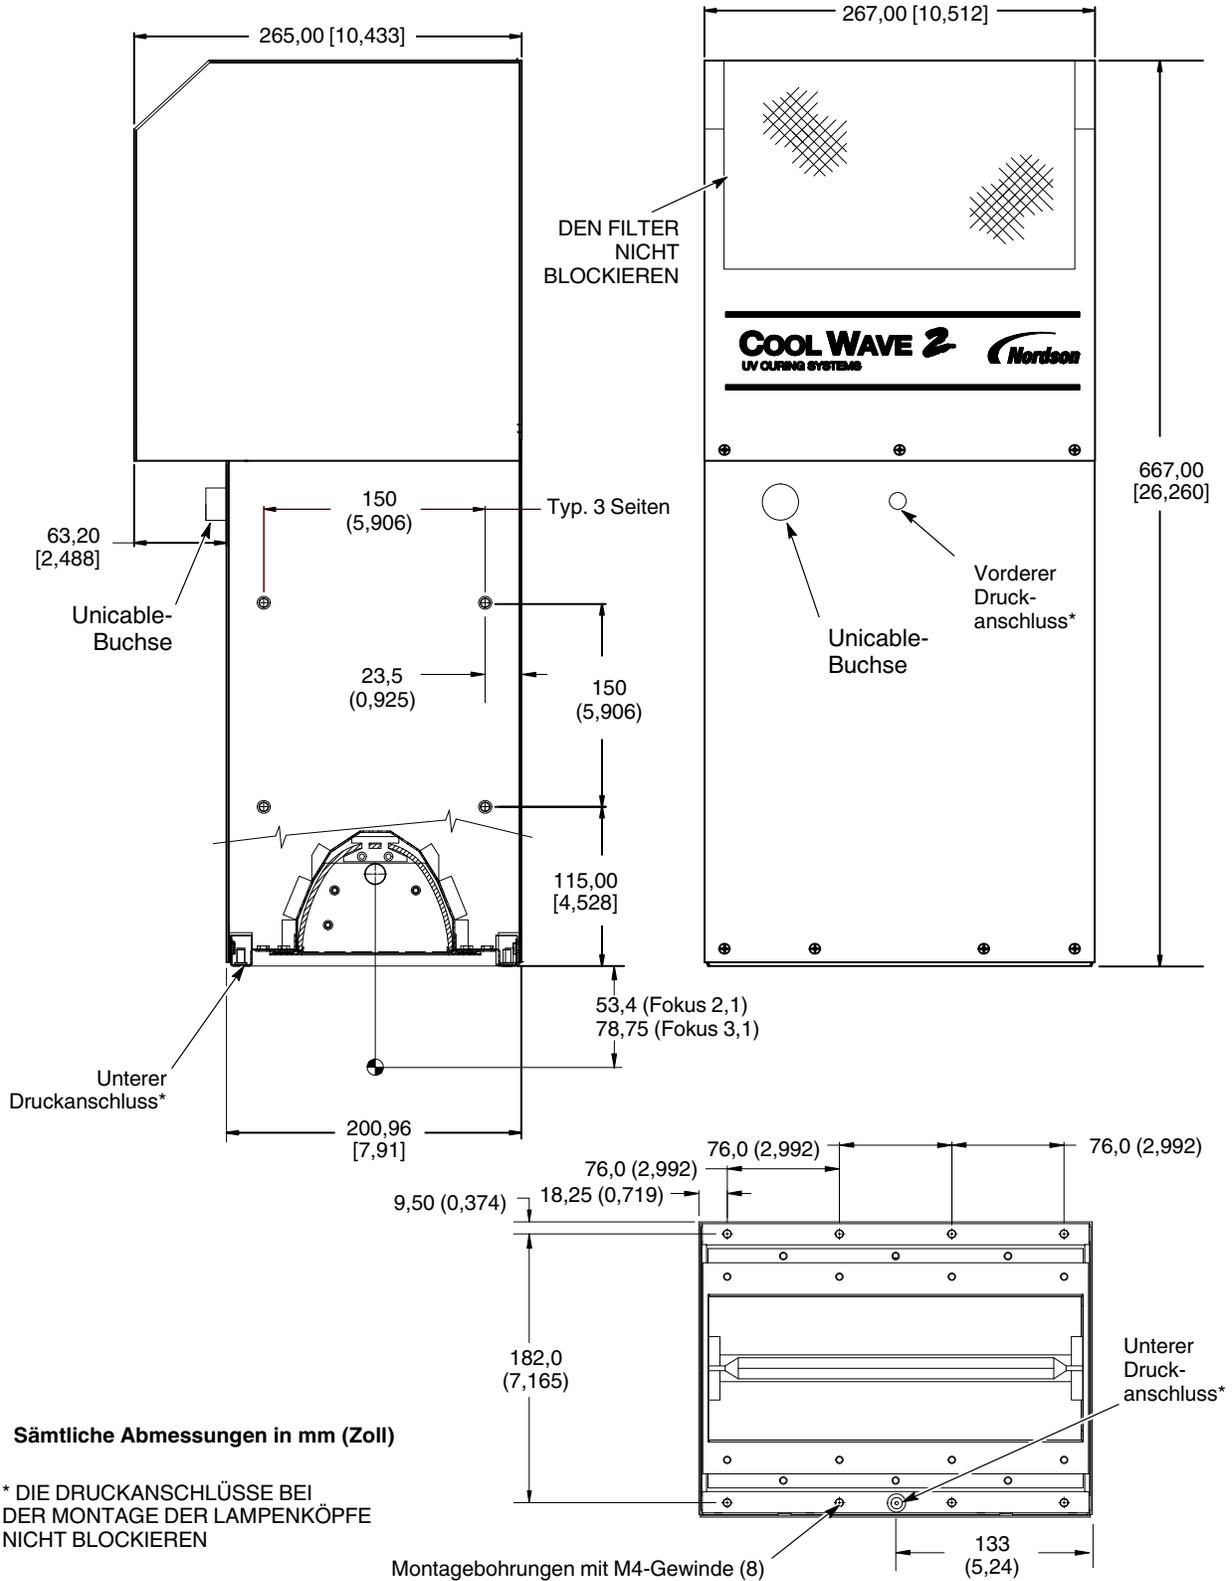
Abmessungen, Lampenkopf mit internem Gebläse
